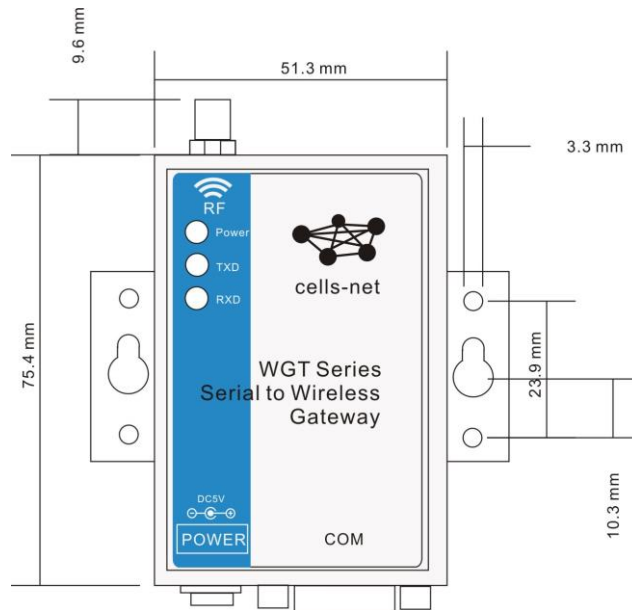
WGT2422Z-R 结构尺寸【俯视图】
